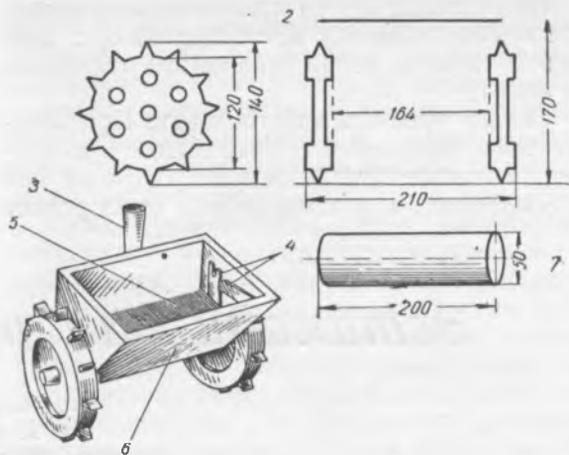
Общий вид сеялки: 1 — колесо с шипами (шпорами); 2 — габаритные размеры сеялки; 3 — ручка; 4 — растяжки крепления щетки; 5 — щетка; 6 — бункер.
